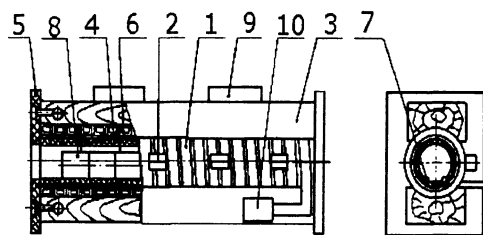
Индуктор кузнечного нагревателя типа КИН, применяемый на МАЗ: 1 — секции; 2 — соединительные колодки; 3 — дубовые брусья; 4 — керамические жароупорные втулки; 5 — асбестоцементная плита; 6 — асбестоцементная прокладка; 7 — направляющие; 8 — заготовки; 9 — водораспределительные колодки; 10 — контактные колодки
